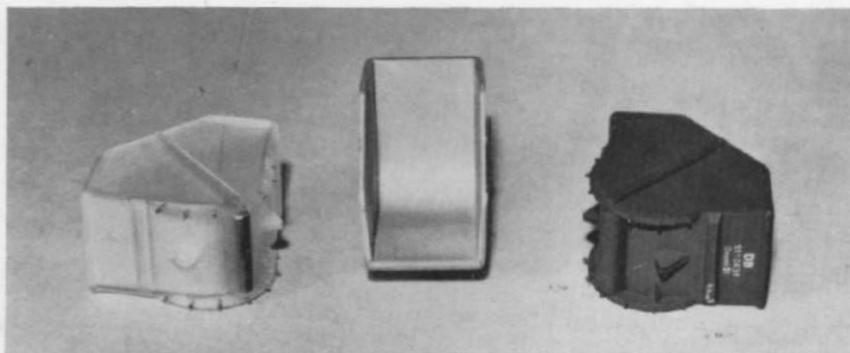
Links: der Gießrohling einer Kippmulde; die miteingegebenen Messingteile sind gut zu erkennen. Mitte: das makellose Innere des Urmodells. Rechts: eine fertig bearbeitete, farbgespritzte und beschriftete Kippmulde.
